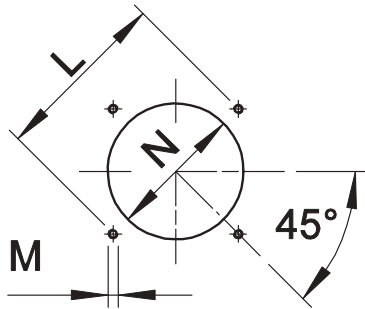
GAS P1800/M-LX-FGR-EL 外形尺寸
